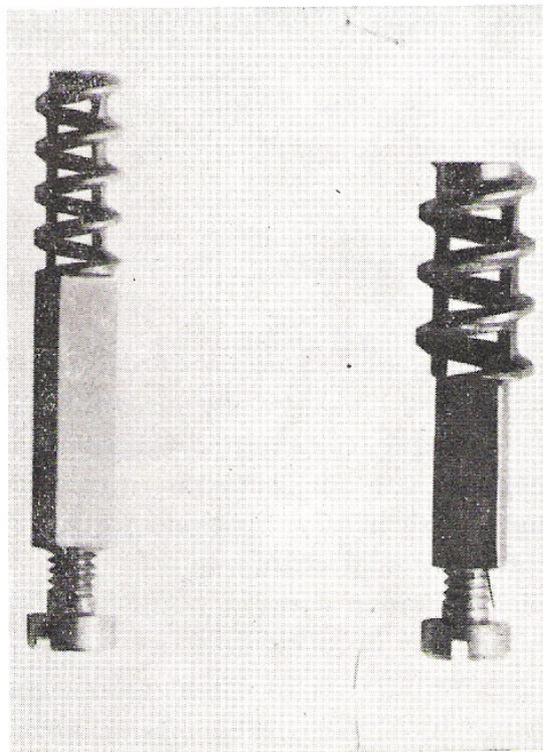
Vite Muratori. (da 3 e da 4 mm.)
